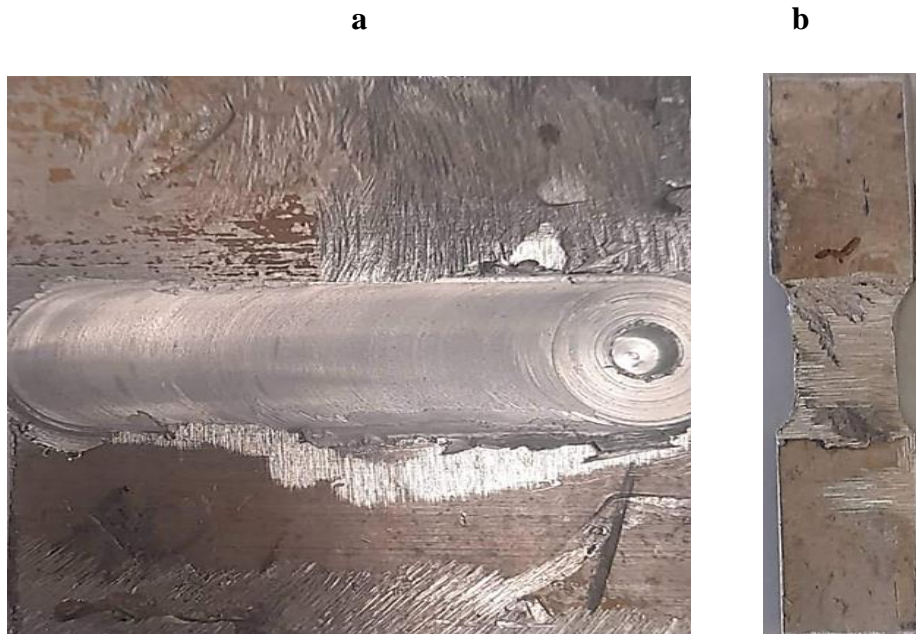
Plaques soudées bout à bout (a). Eprouvette de traction (b).
